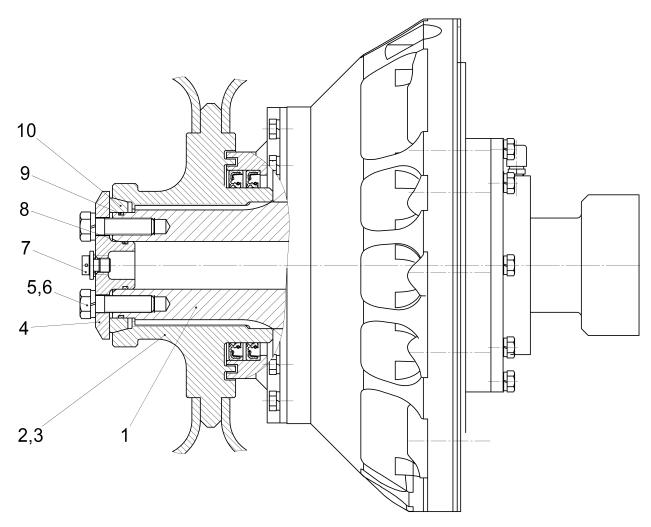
Передача бортовая 3903-2607010 и колесо ведущее
